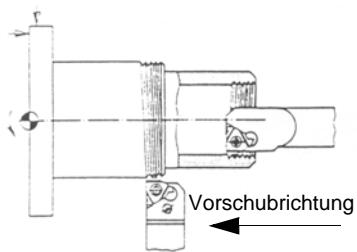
Rechtsgewinde bei Rechtslauf der Maschinenspindel
